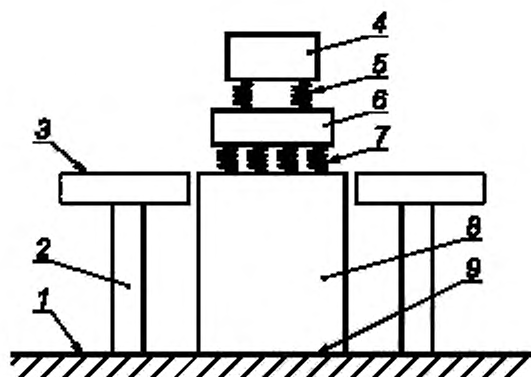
Уруго опертый двигатель, соединенный с безопорным генератором через фланцевый щит
